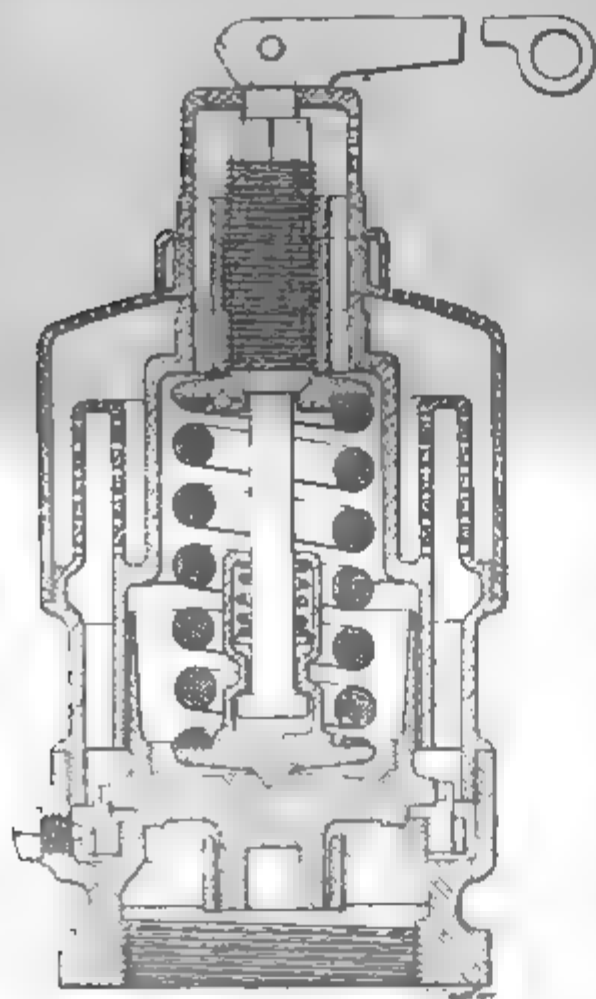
Soupape de sûreté de la Coale Muffler and Safety Valve Co.
